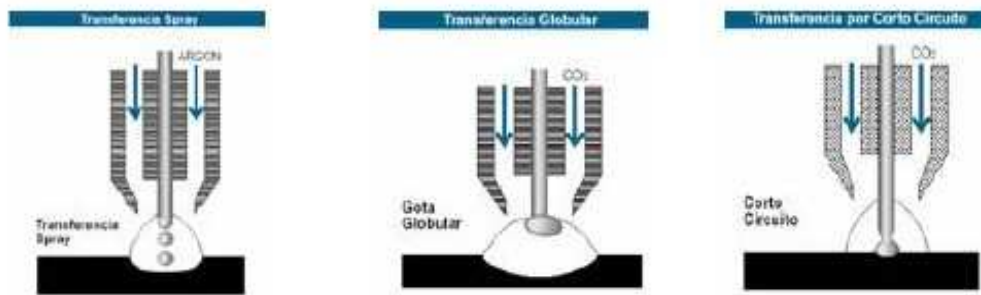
Técnicas del proceso de soldadura MIG.
